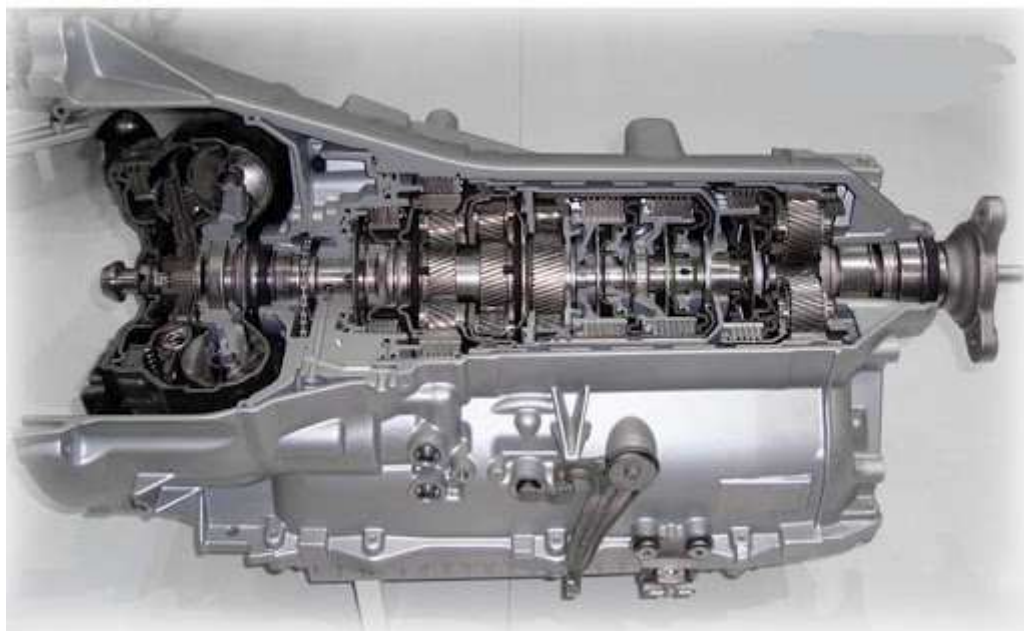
Внешний вид коробки передач ZF 8HP
